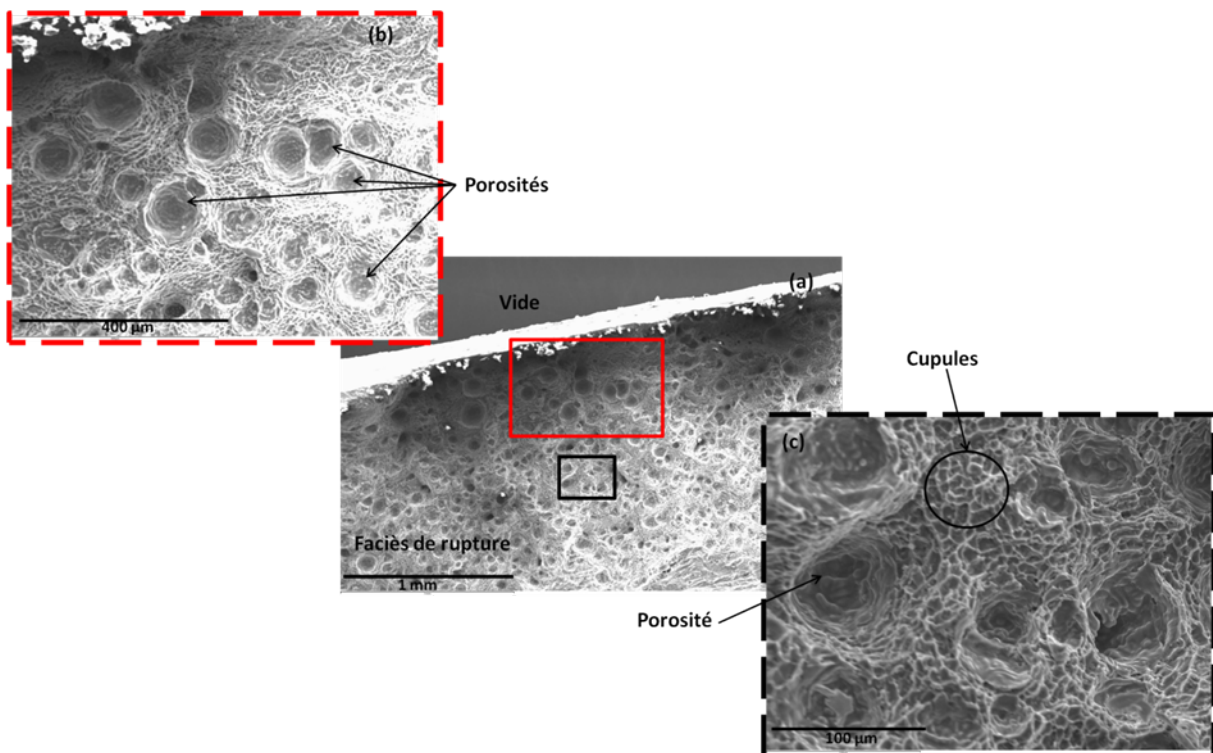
Observation au MEB du faciès de rupture de l'assemblage correspond à la vitesse de soudage de 30 cm/min.
